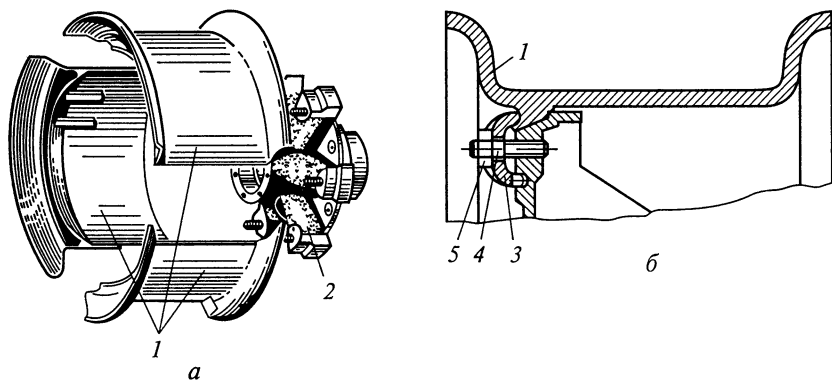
Конструкция (а) и крепление (б) бездискового колеса:
